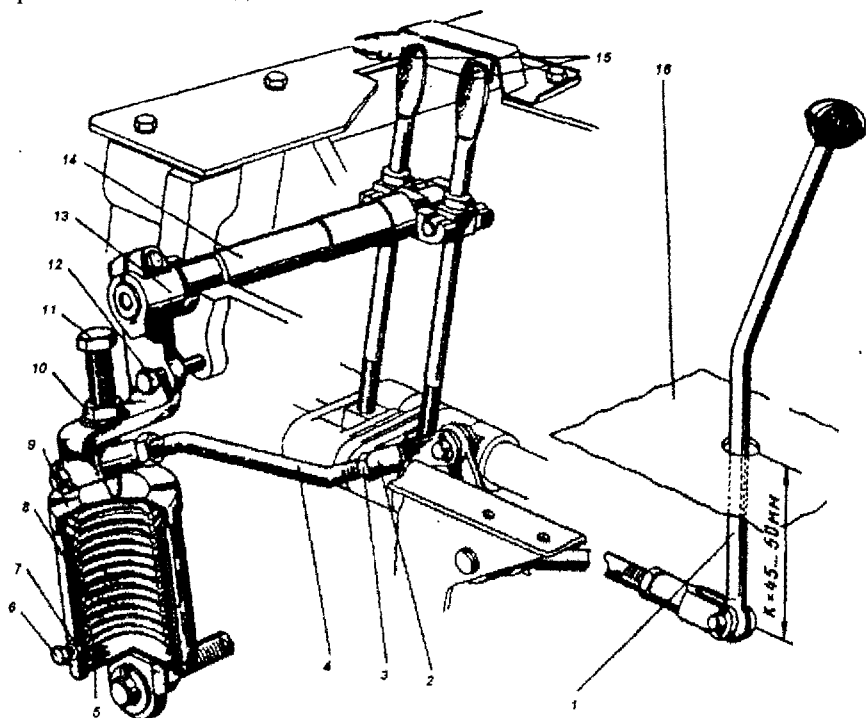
Органы управления задним ВОМ тракторов МТЗ-80, МТЗ-82: 1 - рычаг управления; 2 - регулирующие вилки; 3 - контргайки; 4 - тяга; 5 - стакан пружины; 6 и 7 - болт и гайка; 8 - пружина; 9 - крышка стакана; 10 - контргайка; 11 - упорный болт; 12 - установочный болт; 13 - рычаг; 14 - вал; 15 - регулировочные винты; 16 - полка кабины
